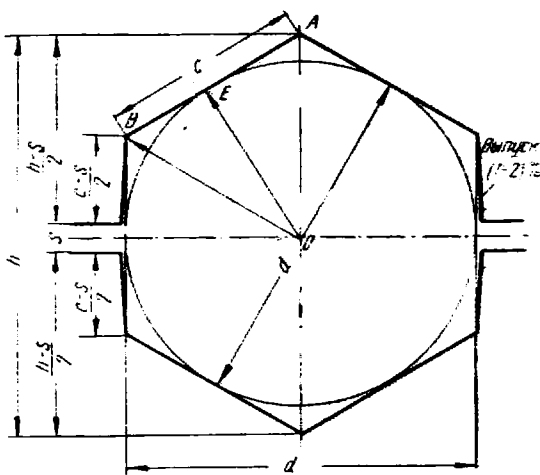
Построение чистового калибра для прокатки шестигранной стали
